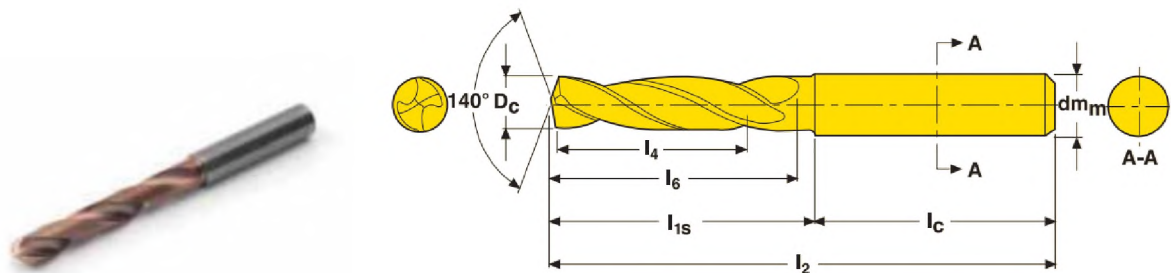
Свердло SD1103-0500-020-06R1 [5, с.25]
